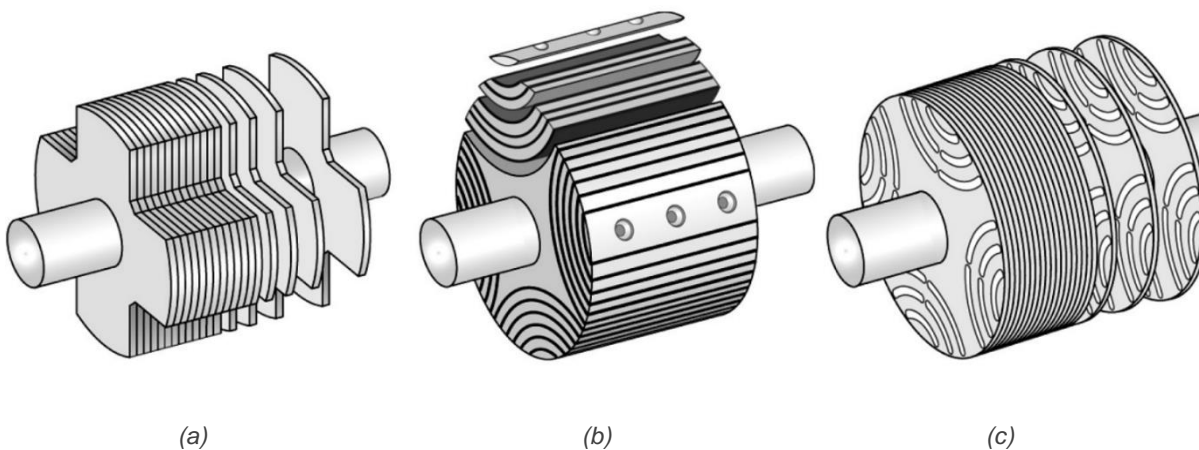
Types de machines synchronéreluctantes, (a) rotor à pôles saillants simples, (b) rotor axialement laminé, (c) rotor transversalement laminé
